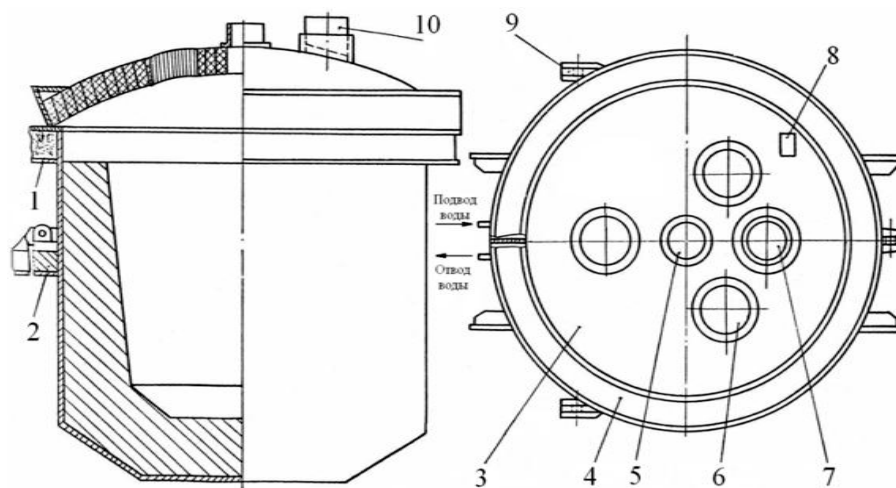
Корпус і склепіння печі СКБ 6063
